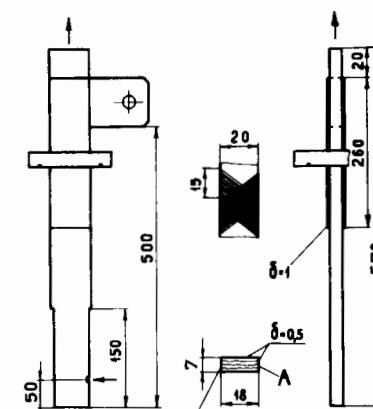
Токоввод на 1,6 кА, А - место сварки.
